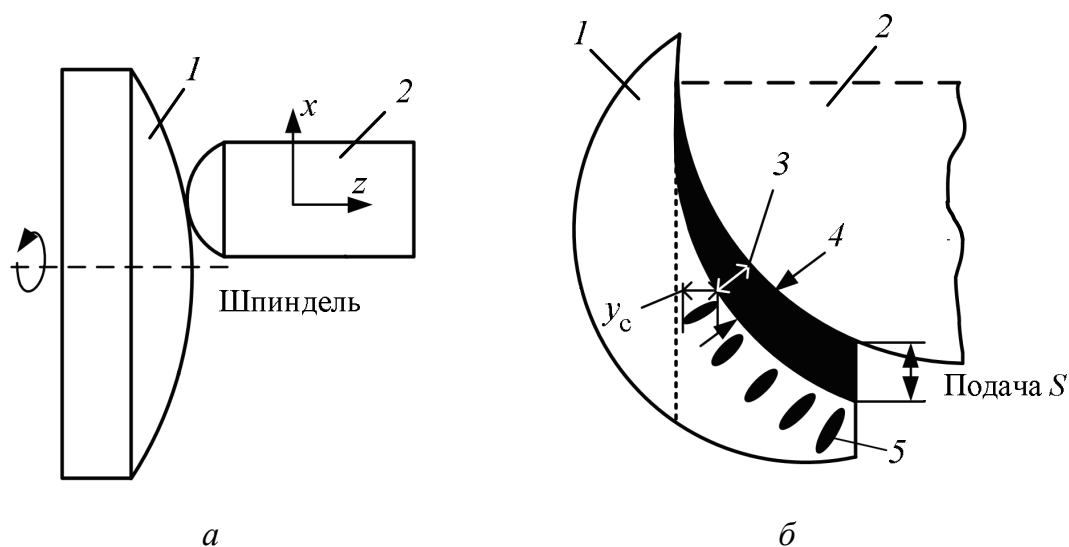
Схематические модели обработки асферической поверхности инструментом с дуговой режущей кромкой:
